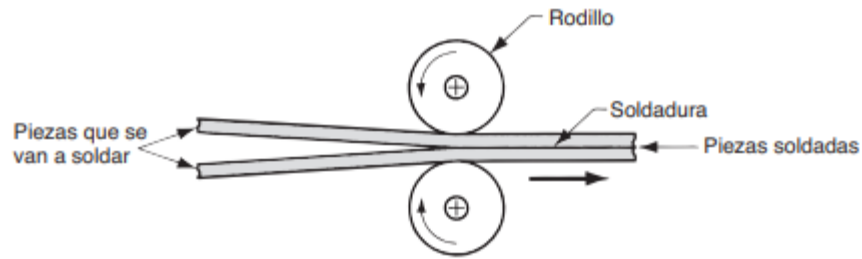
SOLDADURA CON RODILLOS EN FRIO. ADAPTADO DE [71].
